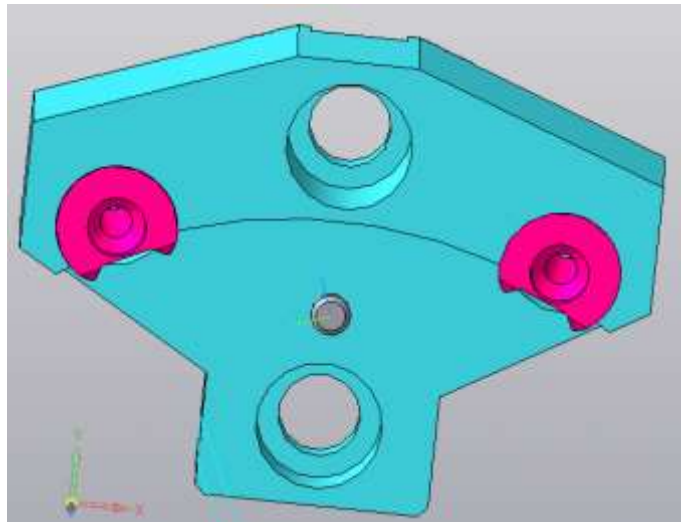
3-д вид та креслення широкого затискного кулачка зі вставками з рифленнями для закріплення по необробленій поверхні
